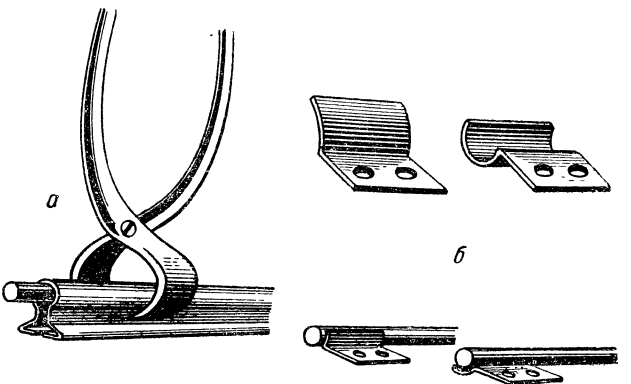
а — загибка заготовки рельса клещами; б — жестяные лапки и их крепление к рельсам из проволоки
